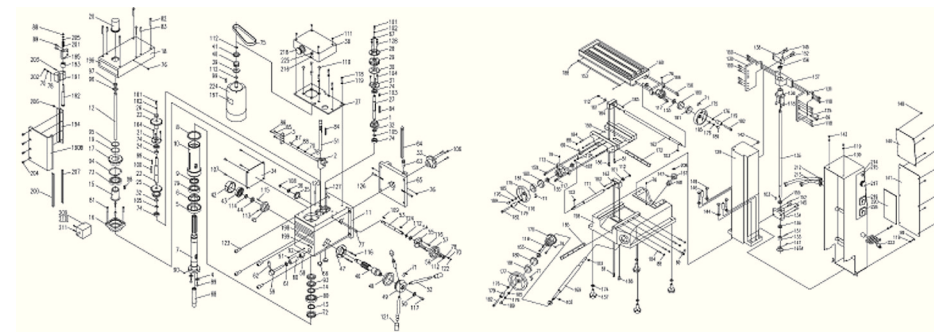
Устройство и схема сборки вертикально-фрезерного станка
